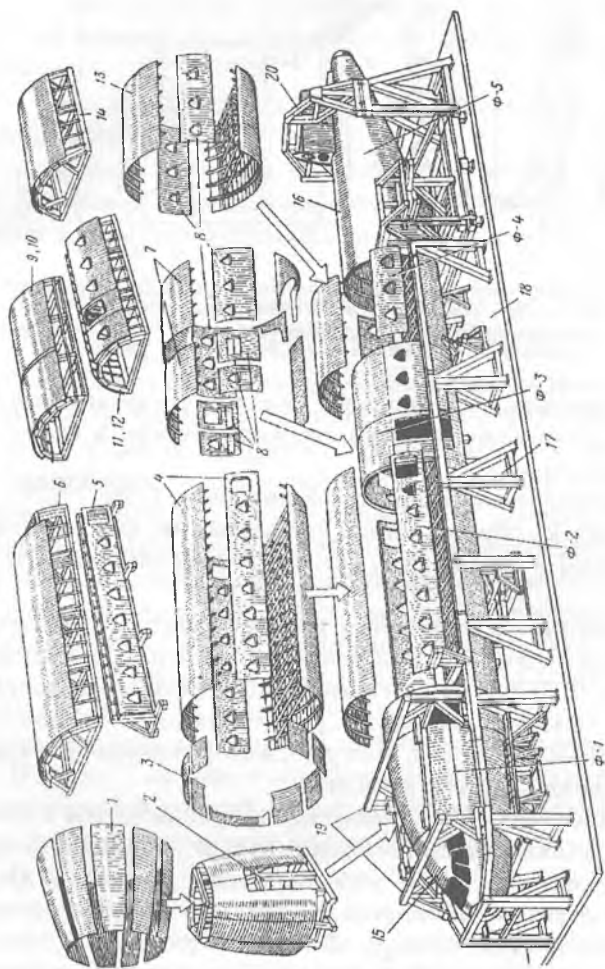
Сборка фюзеляжа самолета панелированной конструкции: 1 — панели Ф-1; 2 — приспособление для сборки Ф-1; 3 и 4 — панели Ф-2; 5 и 6 — приспособление для сборки панелей 3 и 4; 7, 8 и 13 — панели Ф-3 и Ф-4; 9, 10, 11, 12, 14 — приспособления для сборки панелей Ф-3 и Ф-4; 15 — фонарь Ф-1; 16 — отсек Ф-5; 17, 19, 20 — элементы сборочного приспособления; 18 — основание сборочного приспособления
